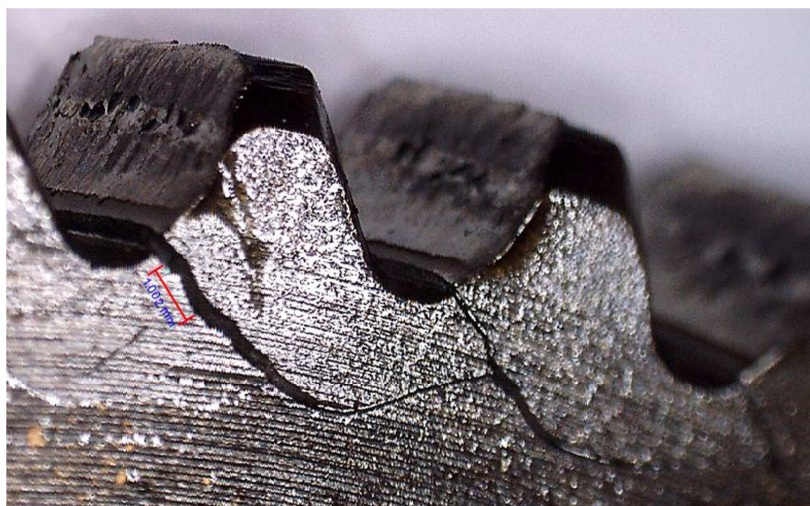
Místa poškození a odlomení zubů pastorku
